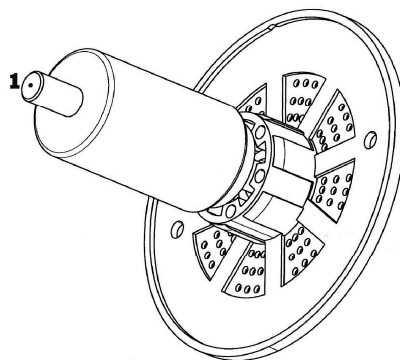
Rotor de ECO Runner incl. plato cubierta
